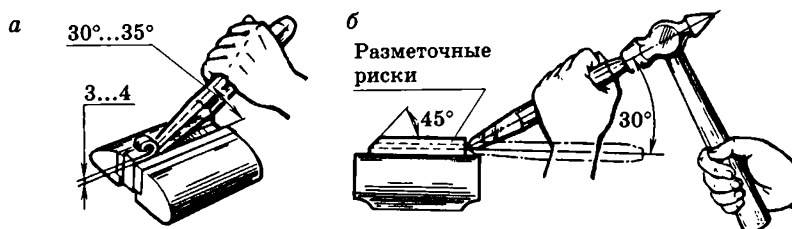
Рубка полосового и листового металла в тисках по разметке
